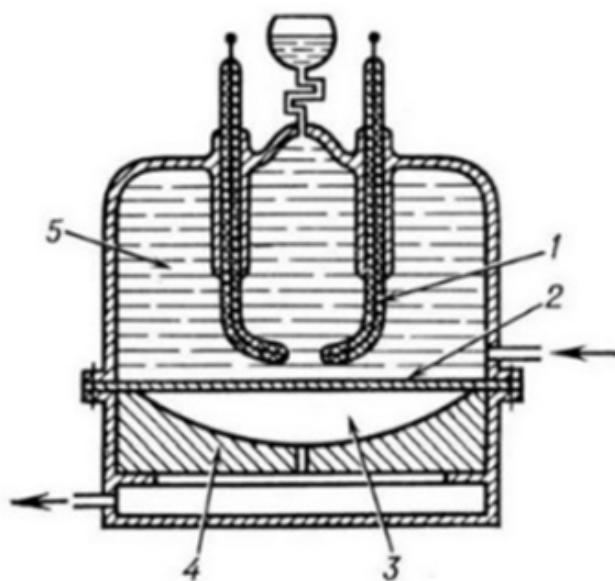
Схема устройства для электрогидравлической штамповки: 1 – электроды; 2 – заготовка; 3 – вакуумная полость; 4 – матрица; 5 – рабочая жидкость
